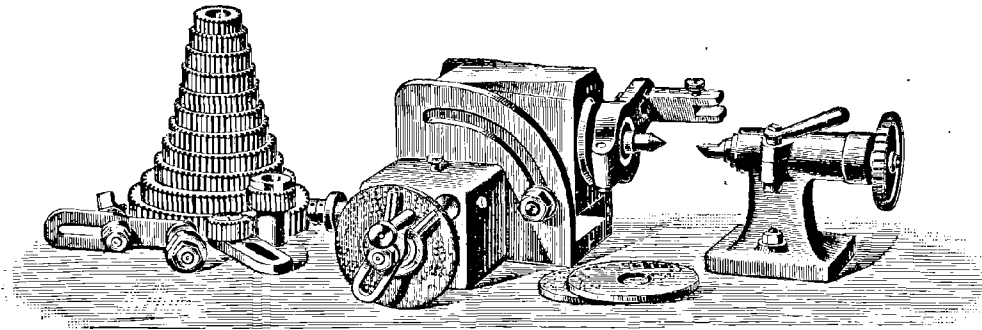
Appareil diviseur universel pour fraiser en hélice.
